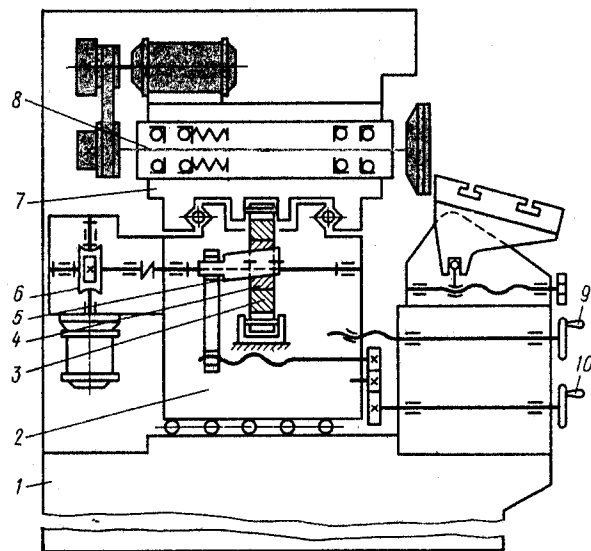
Кинематическая схема заточного станка мод. 3622
